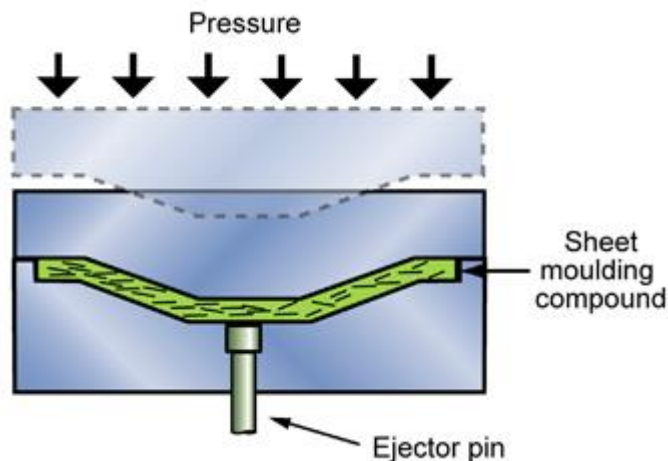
Moldeo por compresión de PPGF (SMC)
